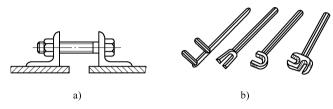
装配夹具 a) 螺旋夹具 b) 杠杆夹具
